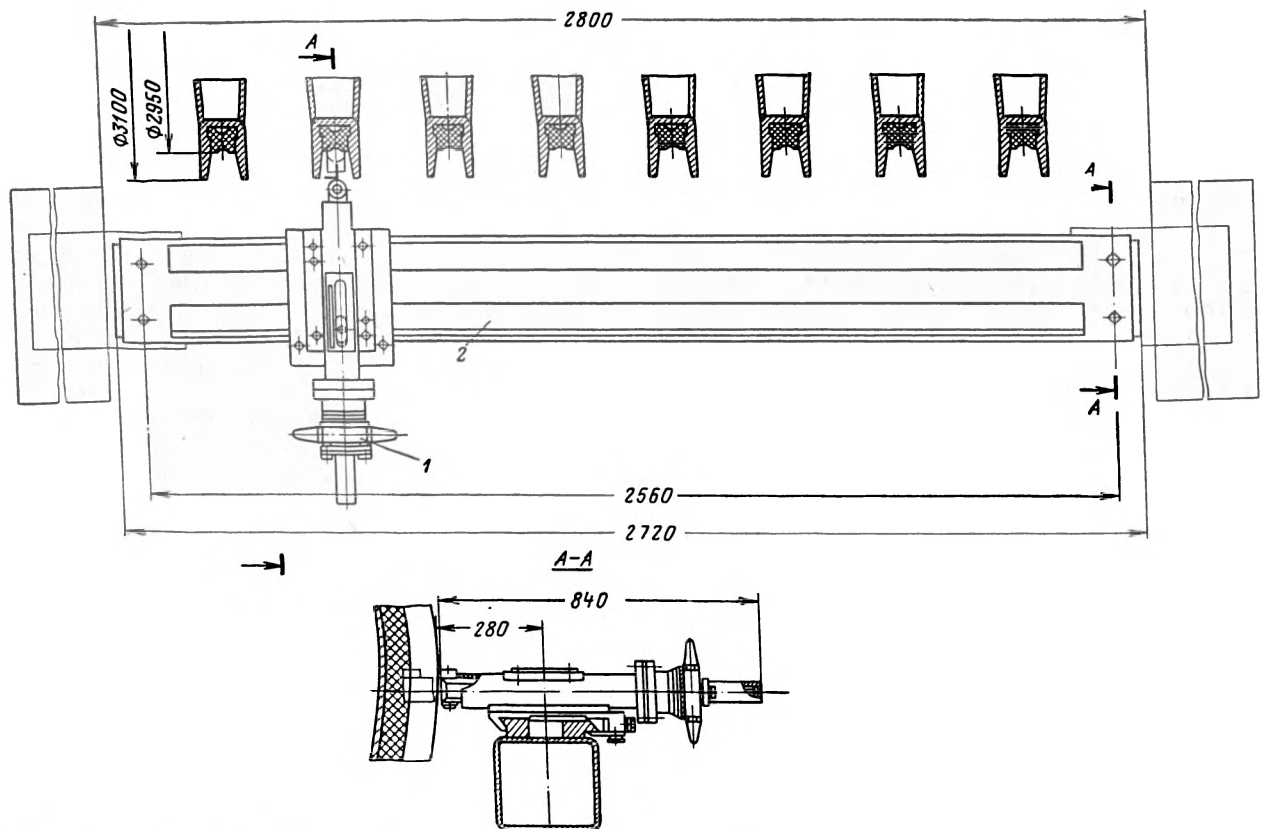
Приспособление для проточки футеровки отклоняющих шкивов
